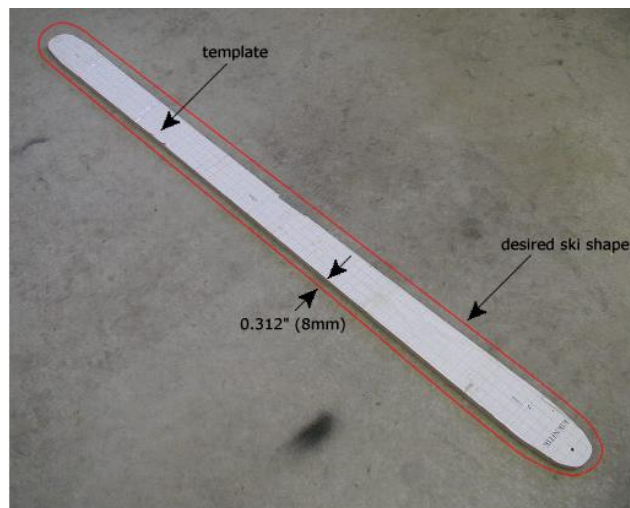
Planta de l'esquí i plantilla reduïda (Skibuilders)
